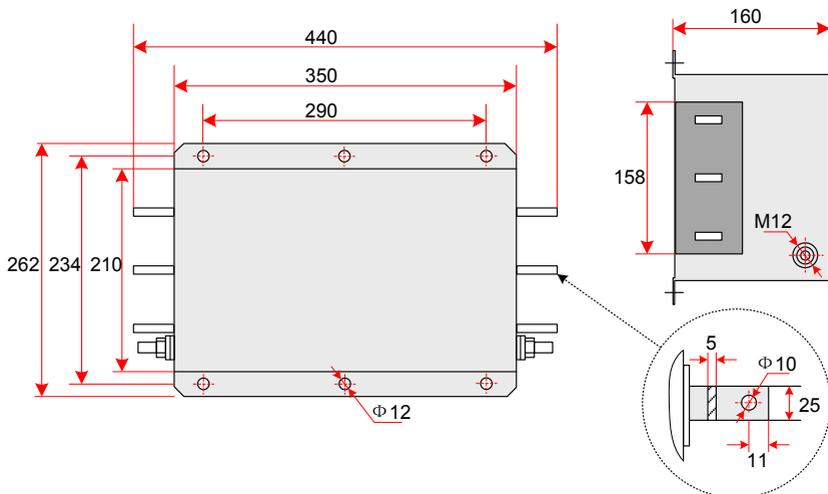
强力滤波器 250A 尺寸图 (单位: mm)
